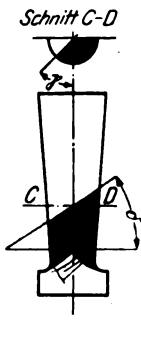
und 6. Druckprobe am kegelförmigen Druckkörper.
